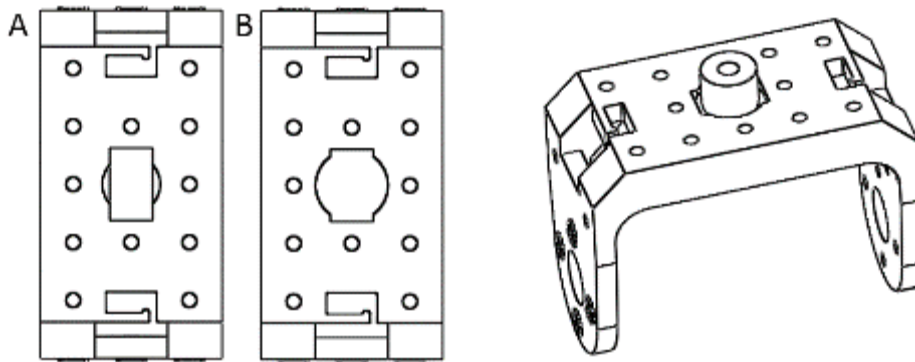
Pieza F2 modificación 1. Izquierda (Vista superior): A) pieza F2 original, B) pieza F2 modificada. Derecha: Ensamble del socket con un buje (BU).
